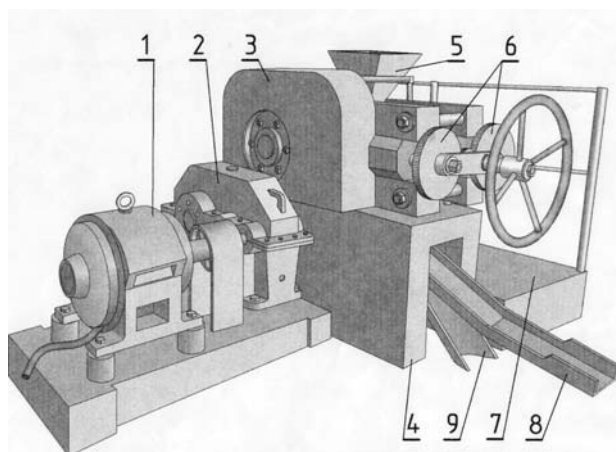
Схема двохвалкового прокатного стану для переробки металевої стружки
